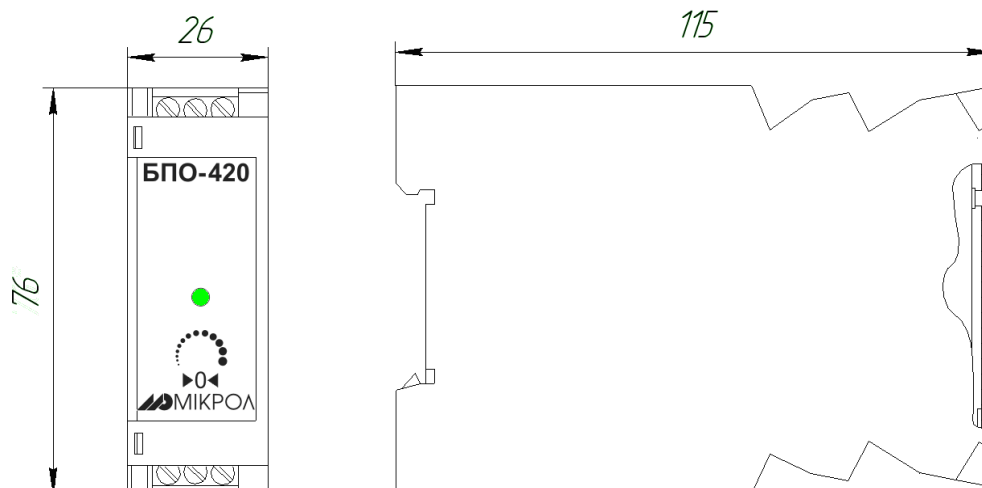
Зовнішній вигляд та габаритні розміри БПО-420
